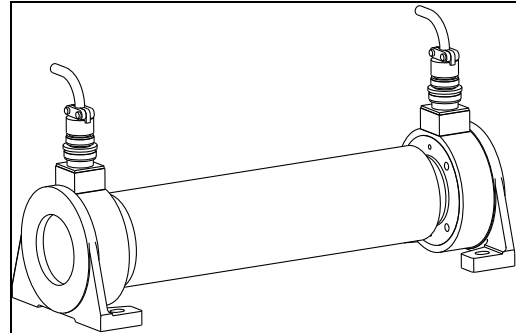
Einbau mit Lagerböcken bei „Inneneinbau“ L000011
